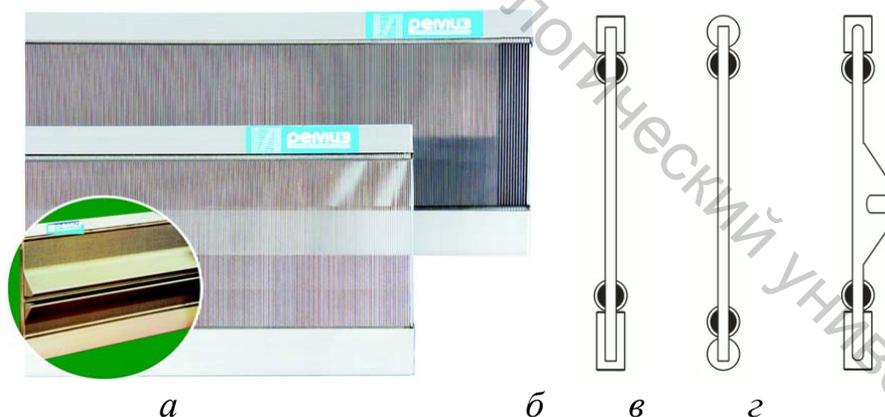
Внешний вид клееных бёрд и схемы зубьев берда с "П" – образными накладками (б), с круглыми накладками (в), с профильным зубом (г)
